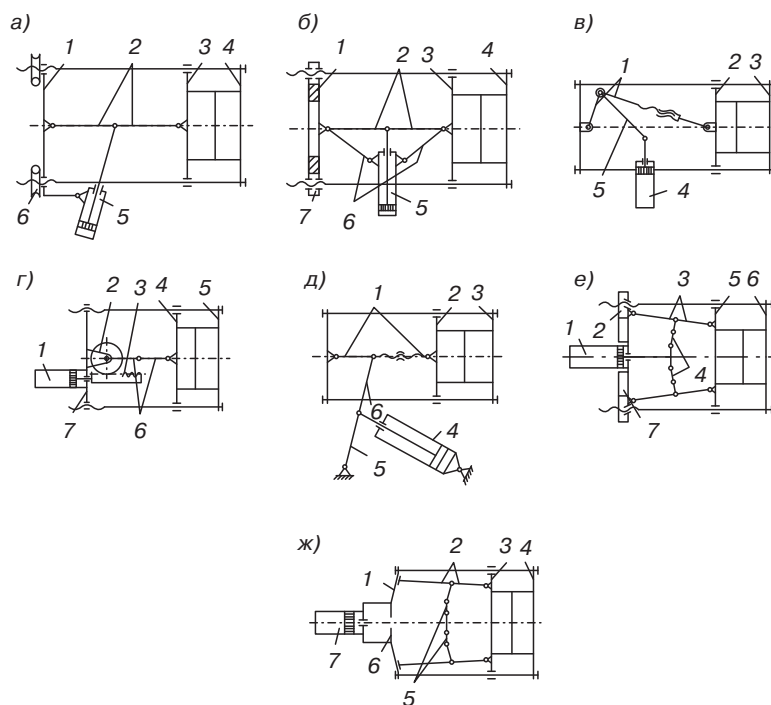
Схемы гидромеханических узлов смыкания форм
